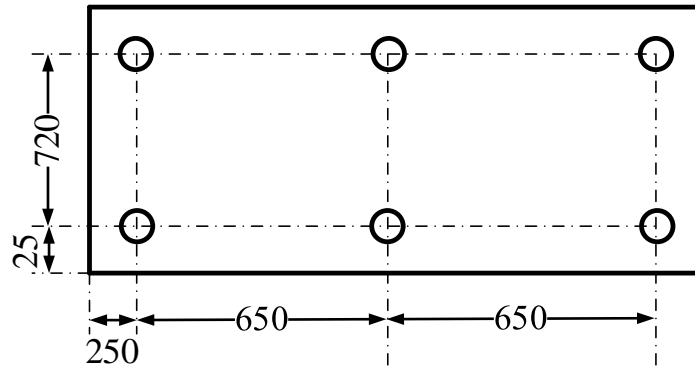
Схема крепления виброизоляторов (вид сверху)
